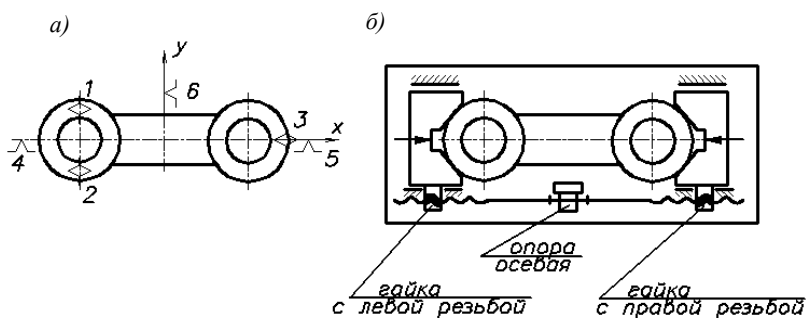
Теоретическая схема базирования рычага и схема конструктивного исполнения приспособления
